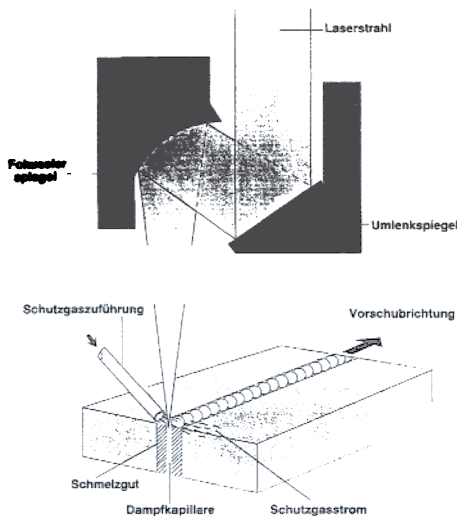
Prinzipbild Laserstrahlschweißen
